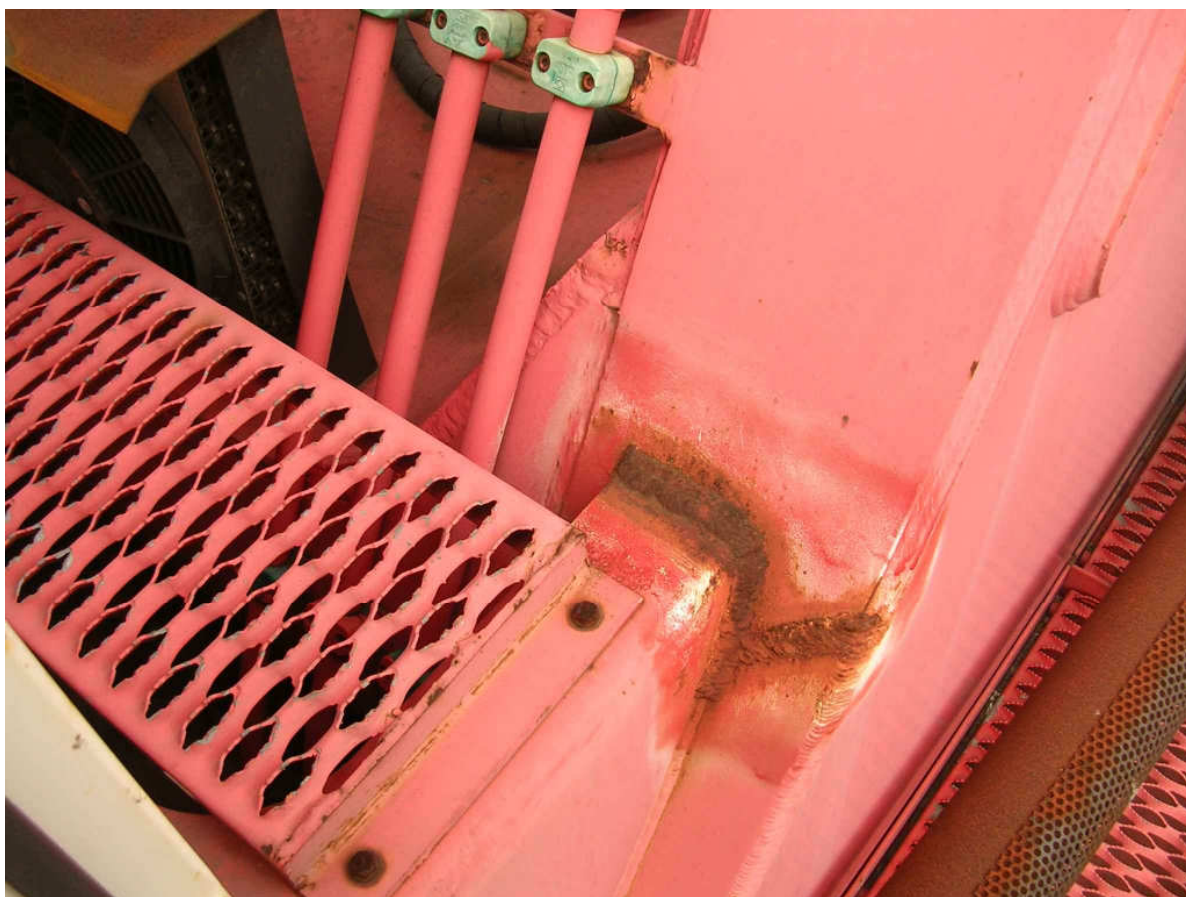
SALDATURE DELLA TORRETTA – N. 610
